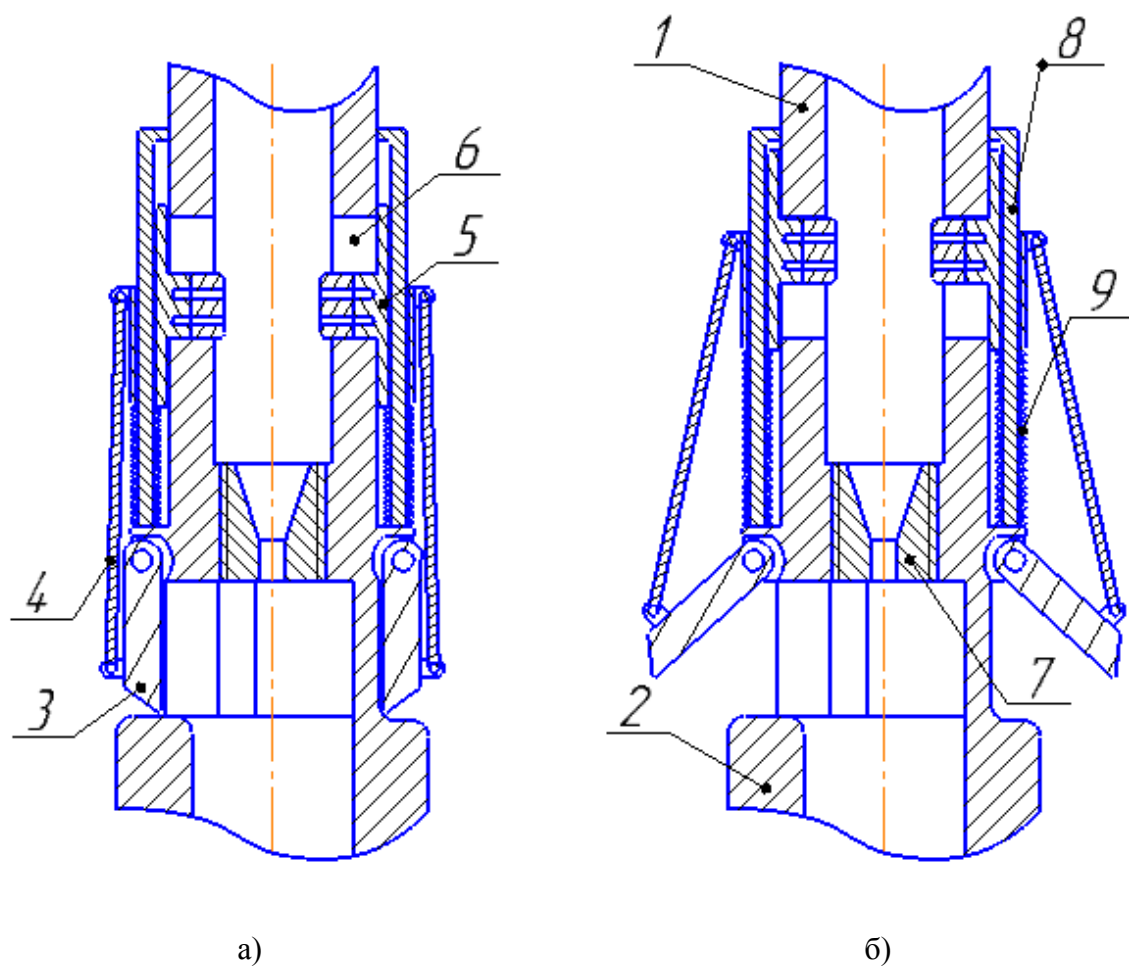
ЗУ с механизмом шарнирно-рычажного типа:
